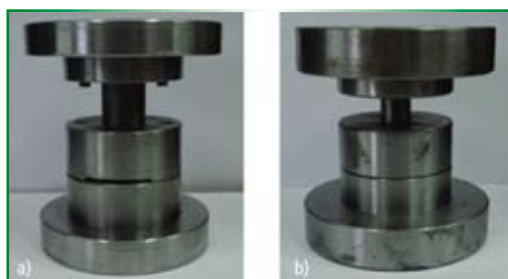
Ferramentas utilizadas para o processo de estampagem do copo: a) ferramenta de corte do blanque; b) ferramenta de estampagem do copo.
